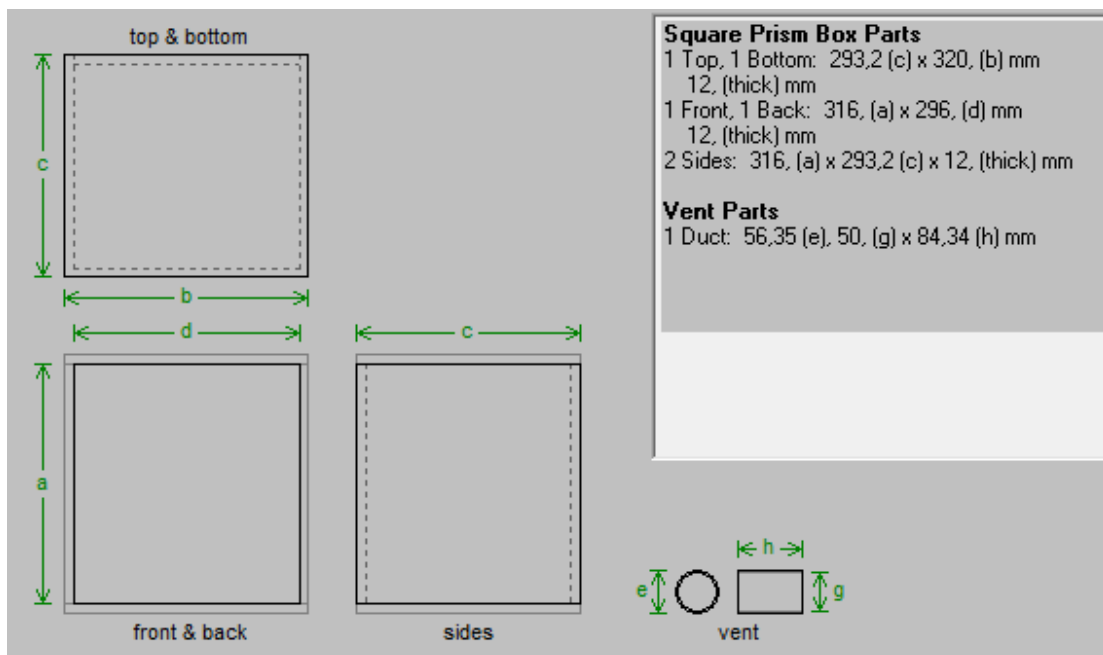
Dimensiones de las maderas utilizadas en la caja acústica
